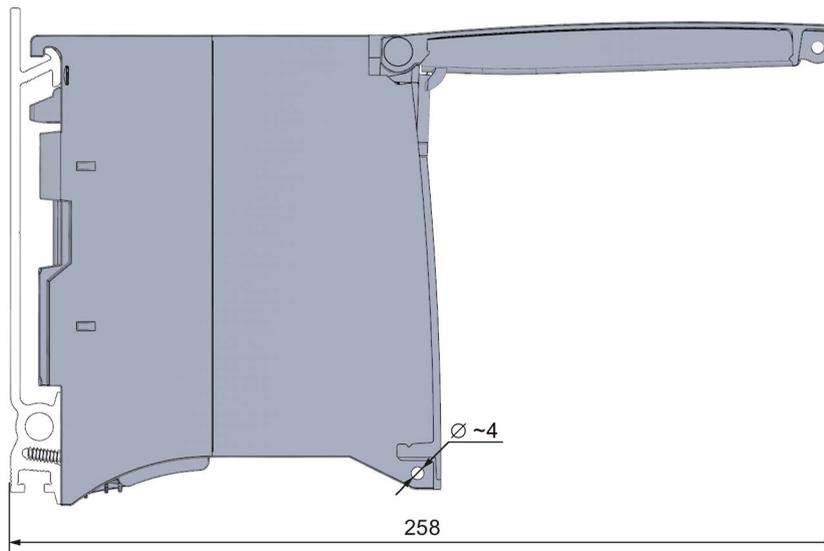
Maßbild CPU 1517-3 PN/DP, Seitenansicht mit geöffneter Frontklappe
